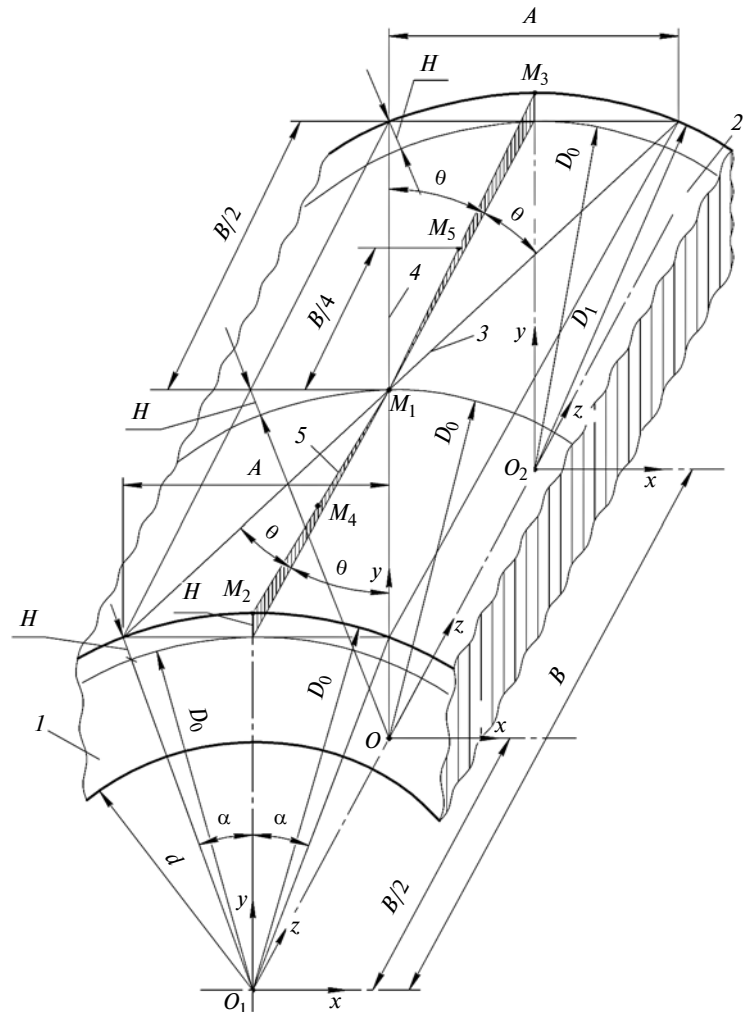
Основные параметры поверхности качения внутреннего кольца предложенного роликоподшипника
